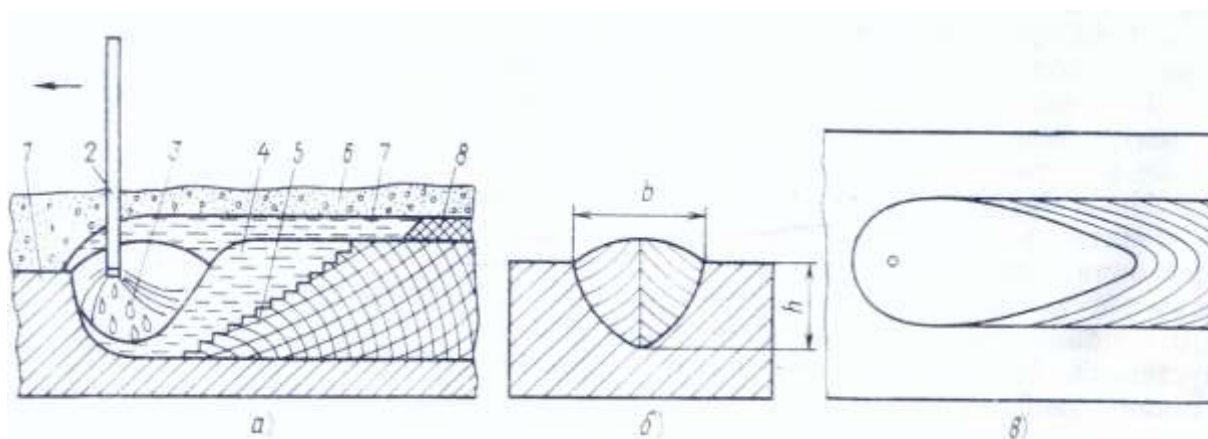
Схема зоны сварки под флюсом: *а* – разрез вдоль оси шва; *б* – поперек шва; *в* – сверху после удаления флюса и шлака.
